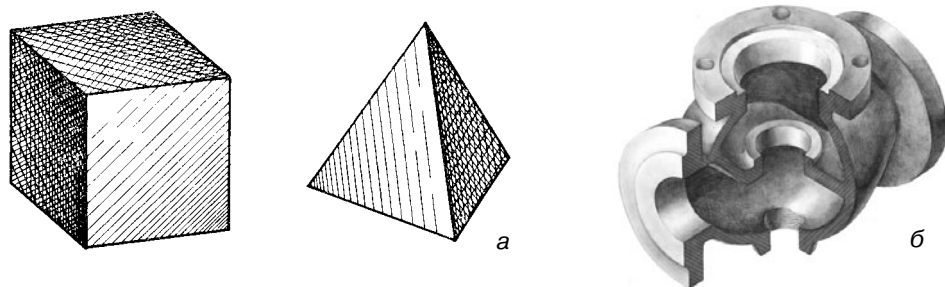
Смешанные способы: а) штриховка + шраффировка; б) тушевка + акварель
